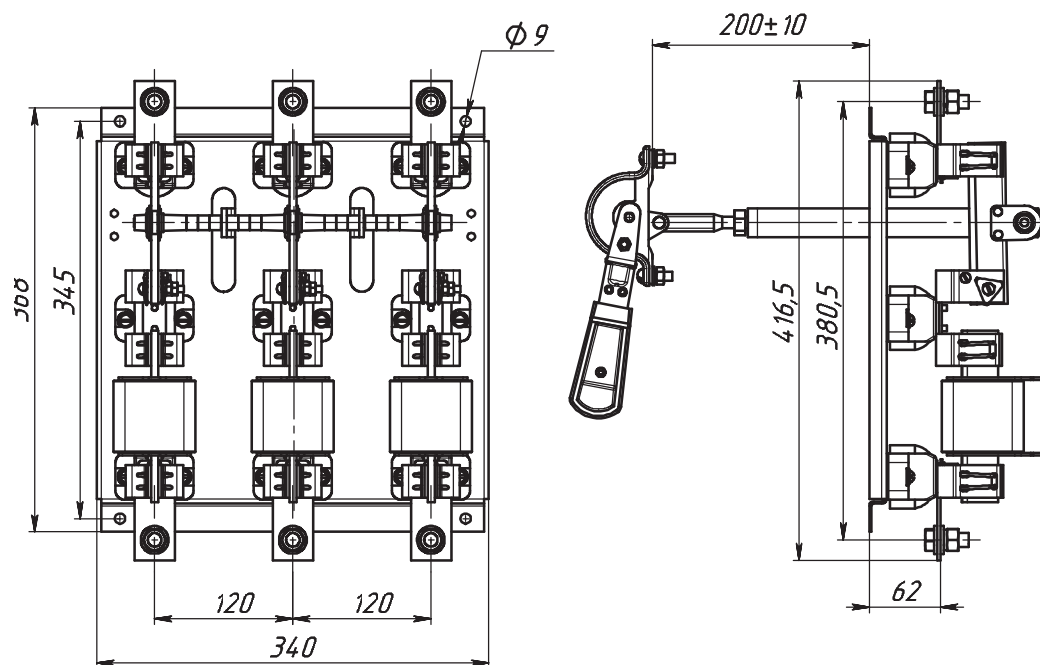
Разъединители-предохранители с центральным приводом на ток 630 А
